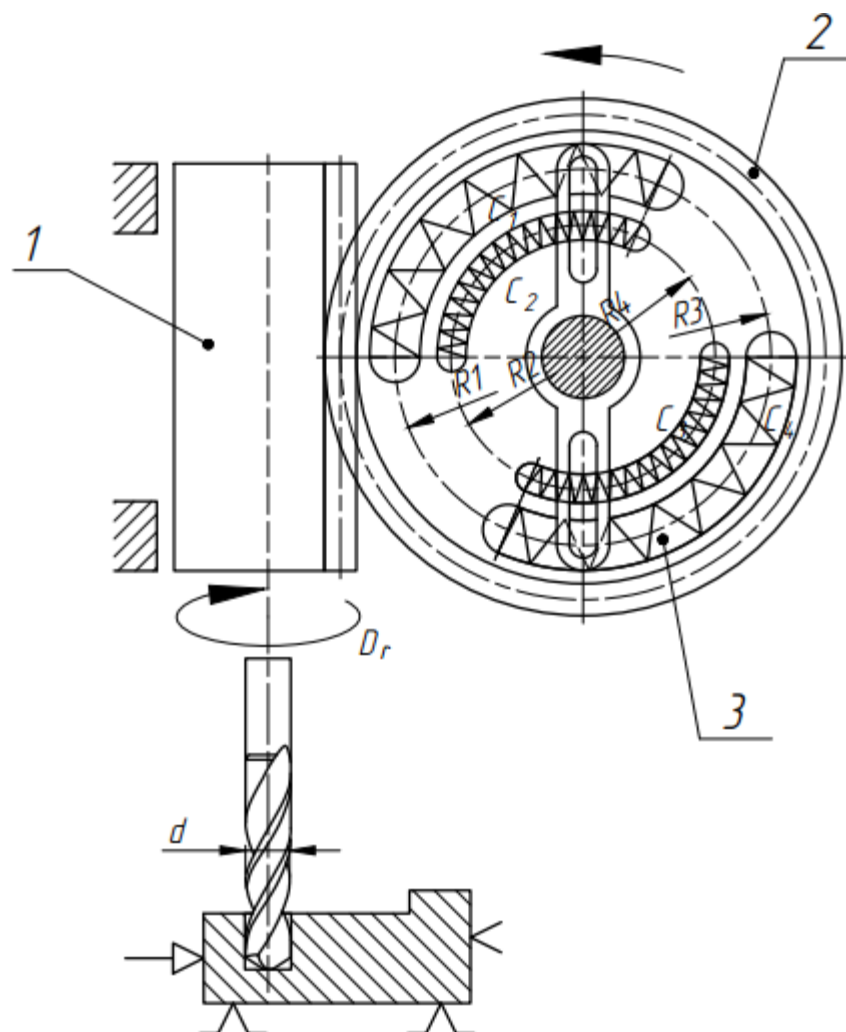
Саморегульований пристрій для свердління із коловим розміщенням пружин
